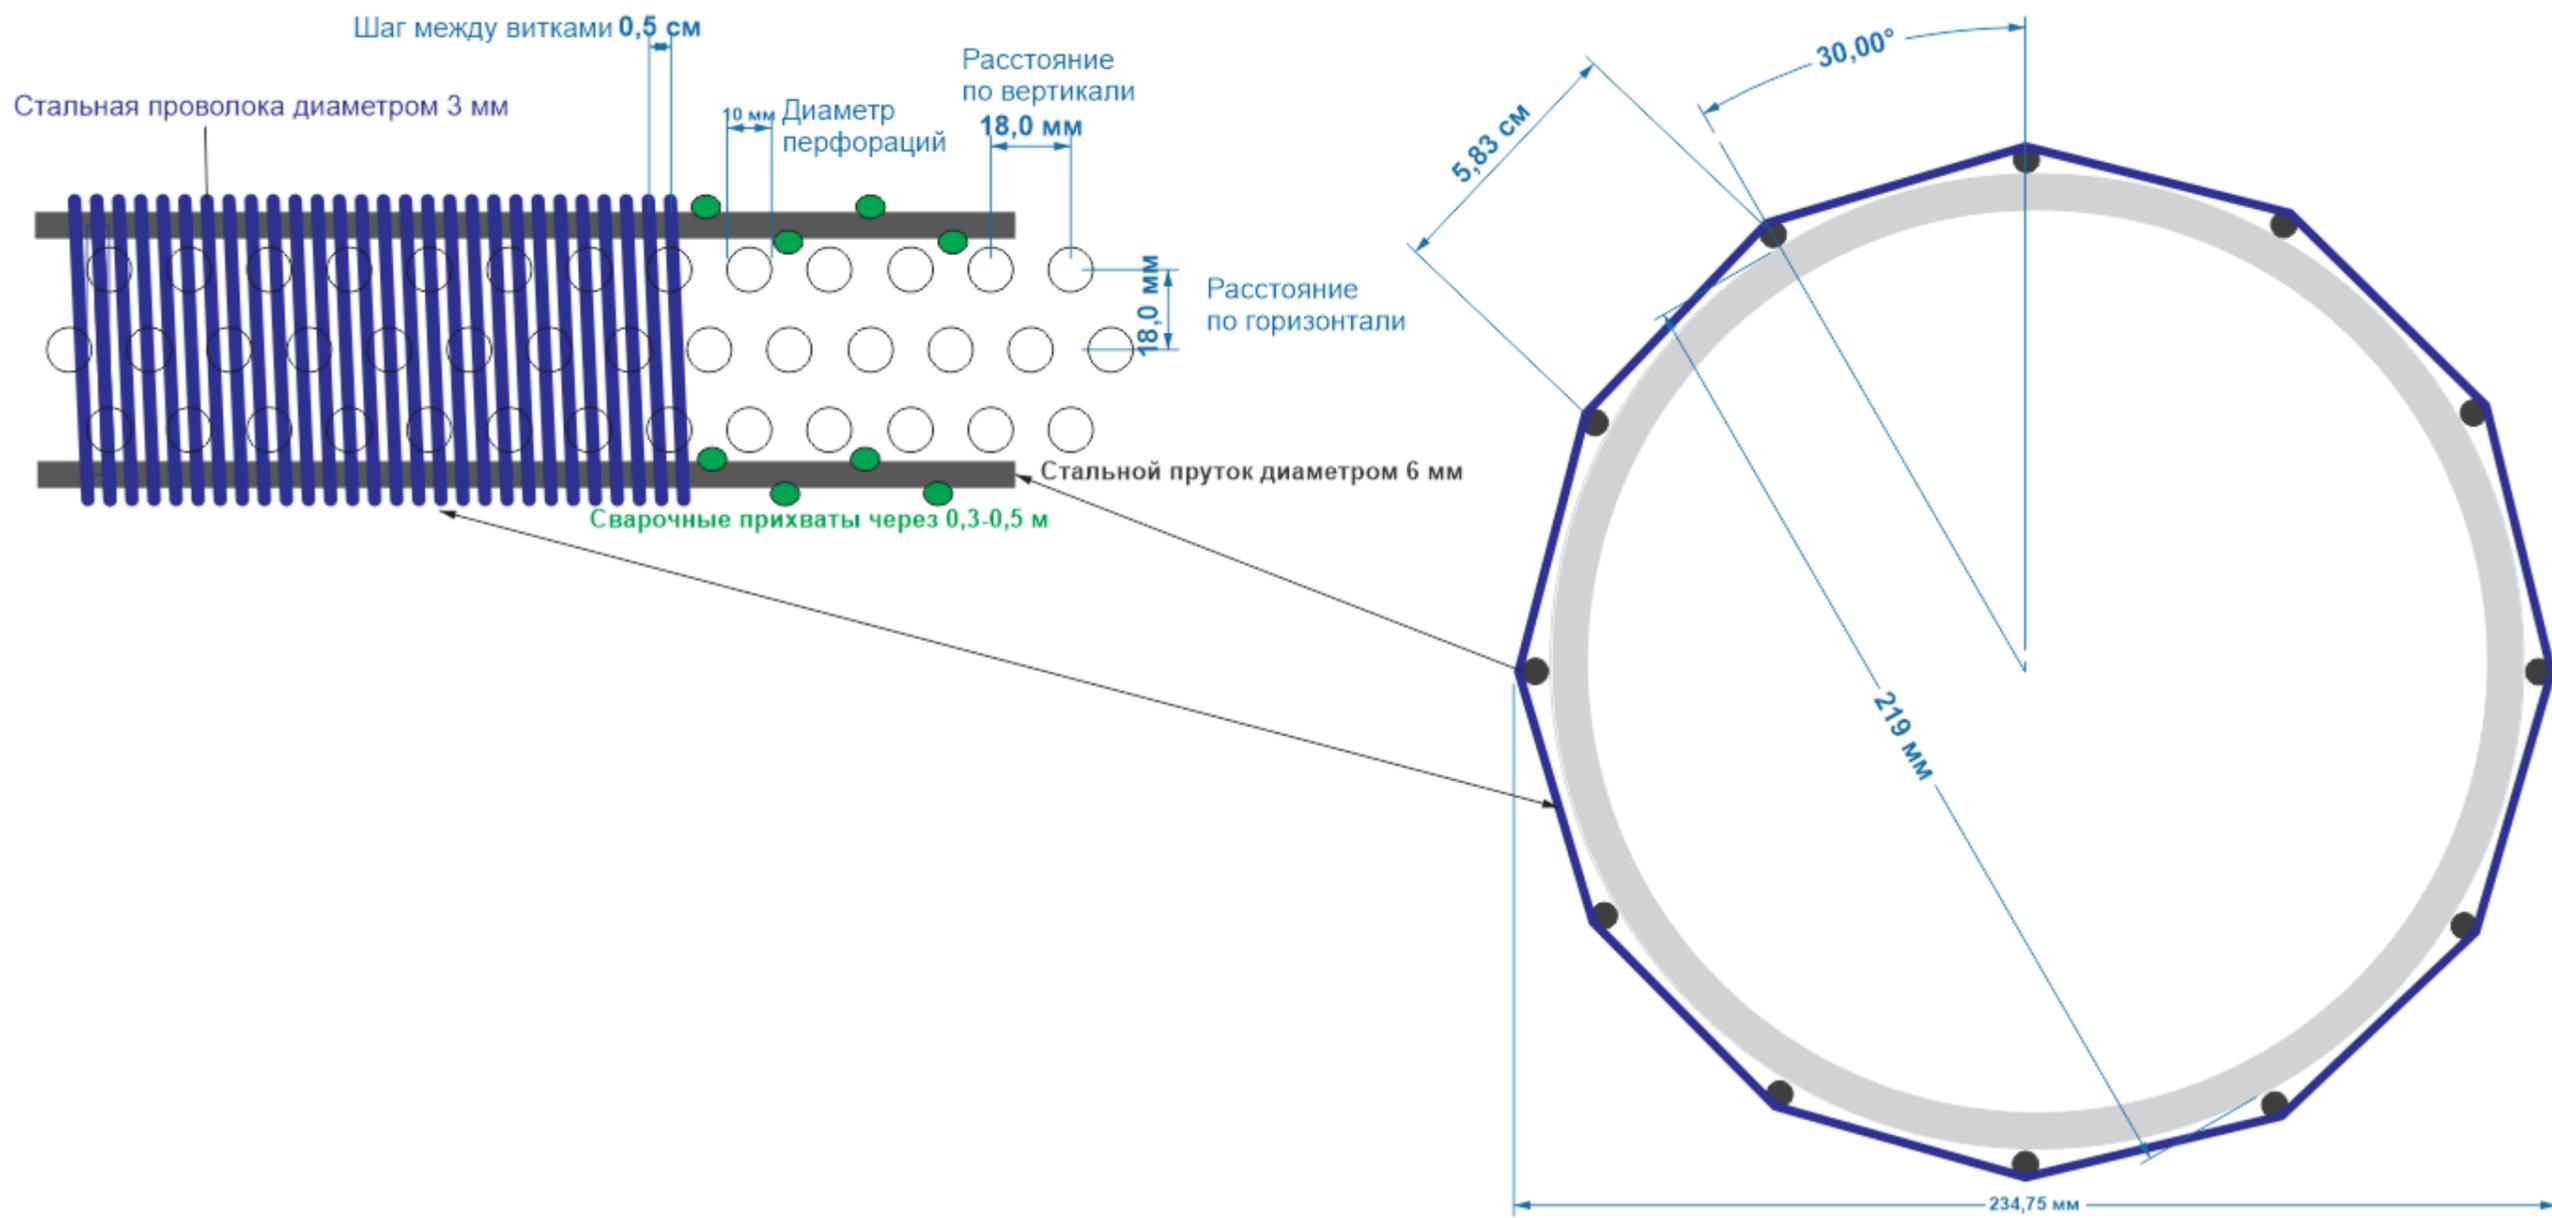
Схема для изготовления проволочного фильтра
